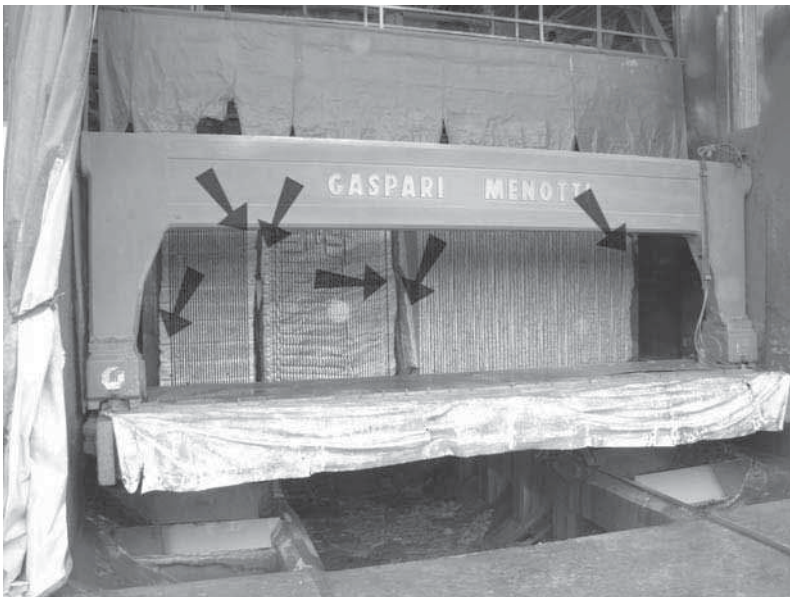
Detalhe dos “casqueiros” das “interas”. (f. autor)
